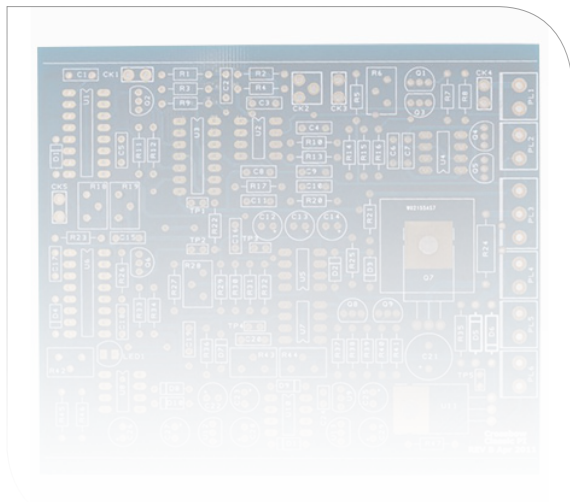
Prototipo di un PCB con due layer (Fonte: PCBWay)
